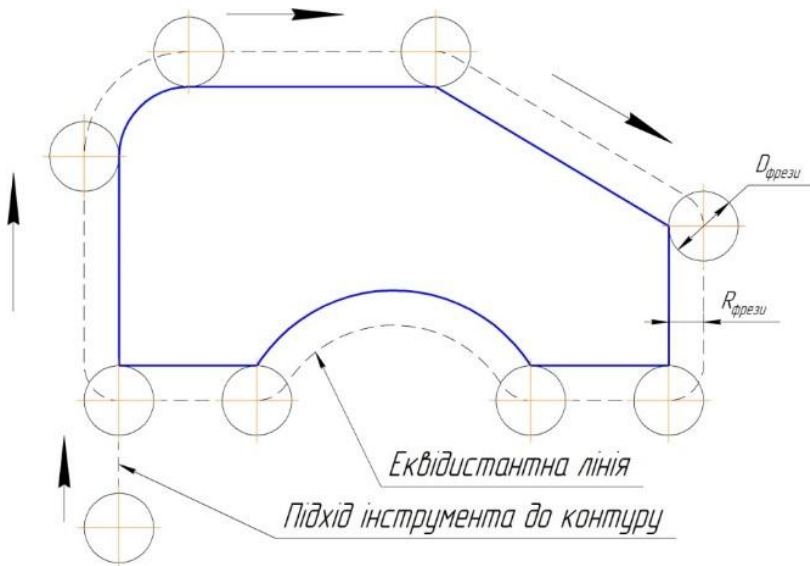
Ілюстрація обходу контуру деталі під час фрезерного оброблення
